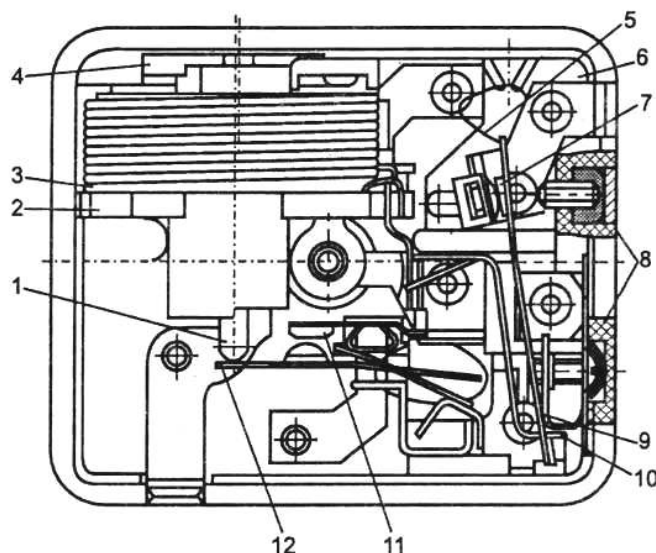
Реле РТП-1: 1 – сердечник; 2 – корпус котушки; 3 – котушка; 4 – фетрова прокладка; 5 – перекидна пружина; 6 – корпус; 7 – контакти теплового реле; 8 – регулювальні гвинти; 9 – біметалічна пластинка; 10 – нагрівальна спіраль; 11 – нерухливий контакт пускового реле; 12 – пластини нерухливого контакту пускового реле
